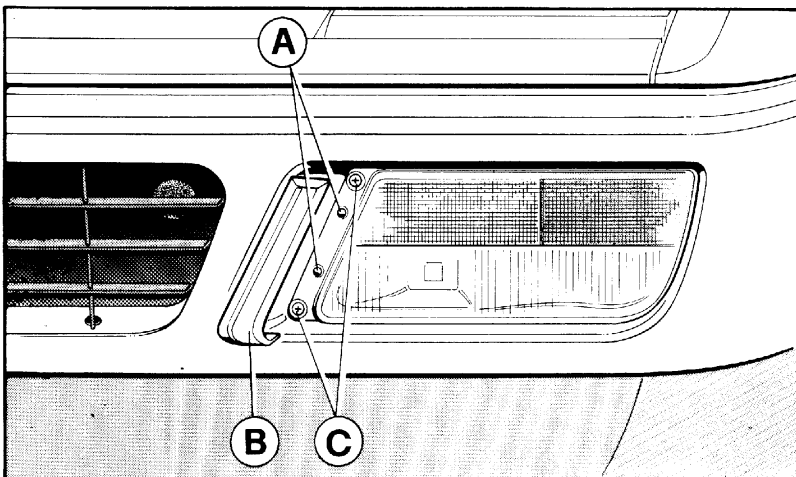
Sostituzione lampada fanale di posizione, direzione e lampeggio
